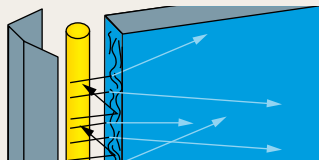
Canto de la plancha rugoso: dispersión parcial en el canto de la plancha.
